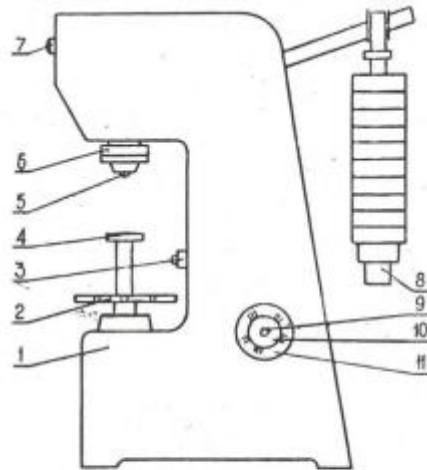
Схема рычажного прессы Бринелля: 1 – корпус; 2 – маховик; 3 – кнопка; 4 – стол; 5 – наконечник; 6 – ограничитель; 7 – сигнальная лампочка; 8 – подвеска с грузами; 9 – винт; 10 – подвижный диск; 11 – неподвижный диск.
